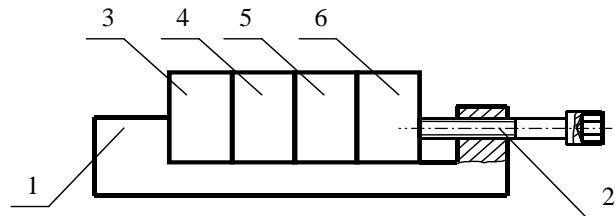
Схема закрепления образцов из быстрорежущей стали Р6М5Ф3 и твердых сплавов на столе плоскошлифовального станка
